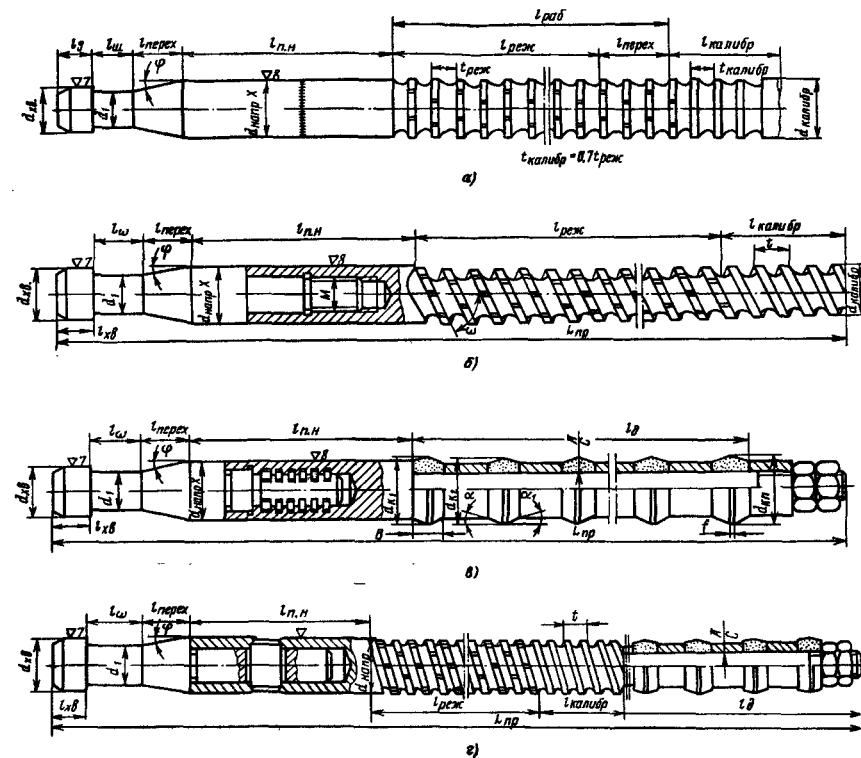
Конструкции протяжного инструмента для обработки точных отверстий в однородных и смешанных пакетах
